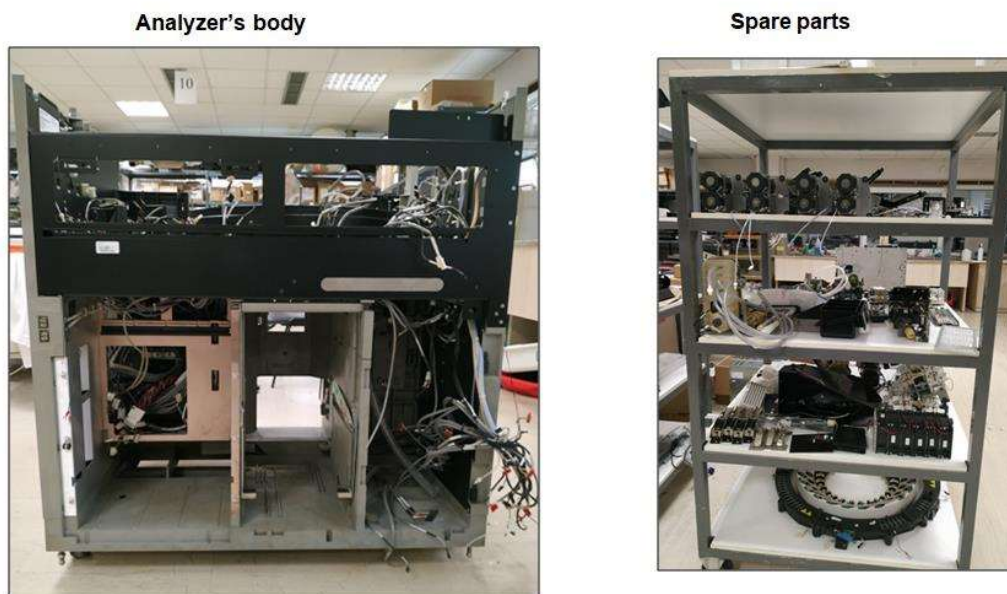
SOP REM 4 Cleaning Part B Disposable & Removable parts Handling
